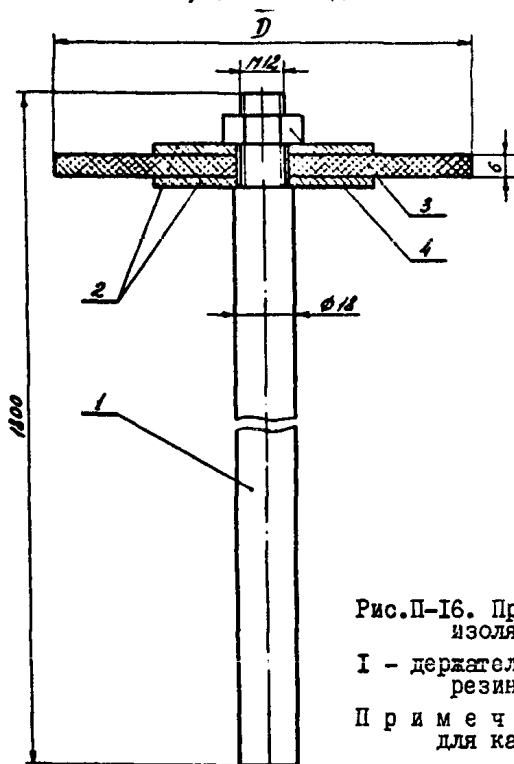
Приспособление для чистки опорных изоляторов камеры и отделителя:
